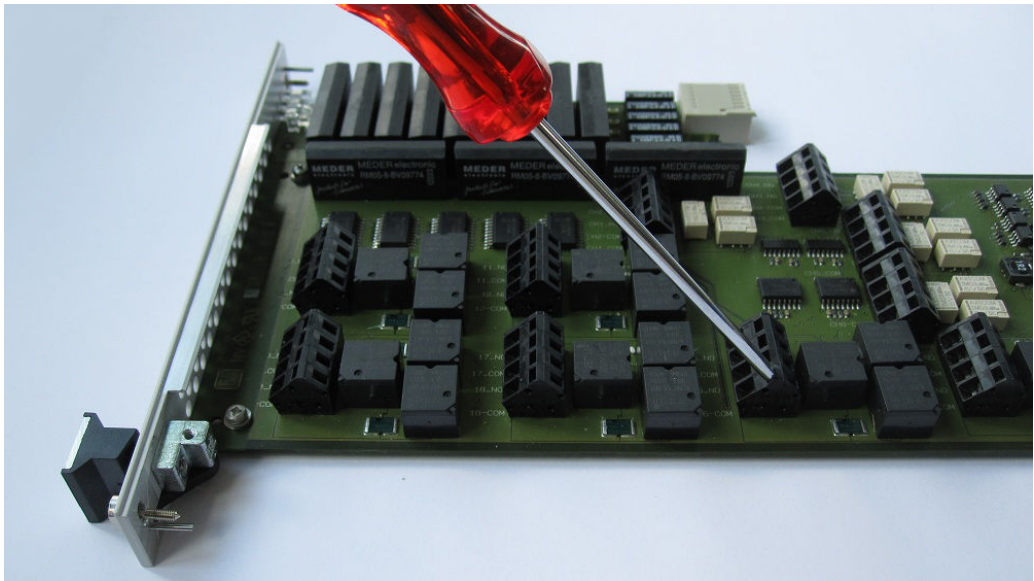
Öffnen des Klemmenkontaktes CH16_COM
